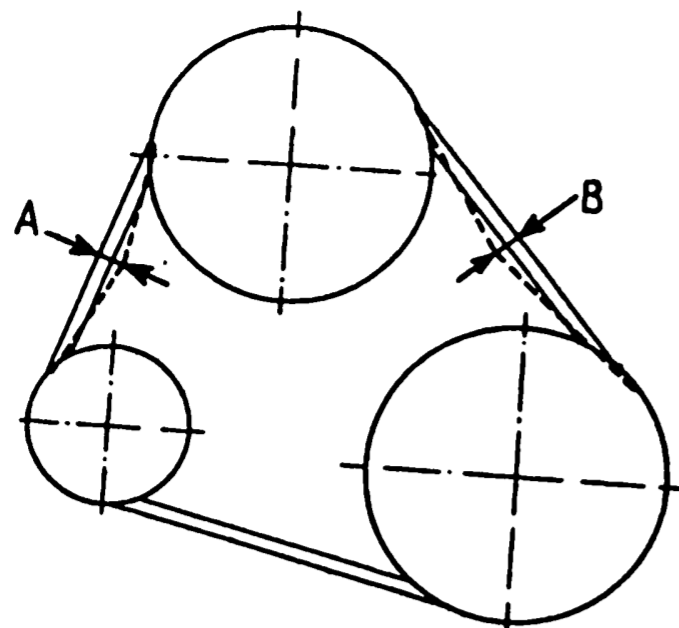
Схема проверки натяжения ремня привода насоса
